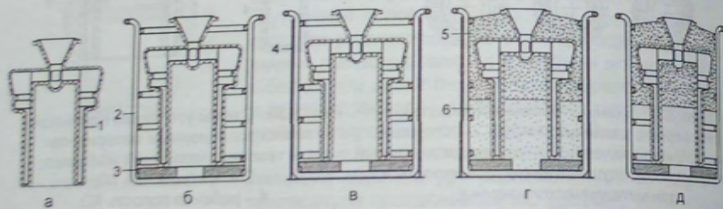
Схема способа утепления прибил путём избирательной упаковки КО в опорный наполнитель
